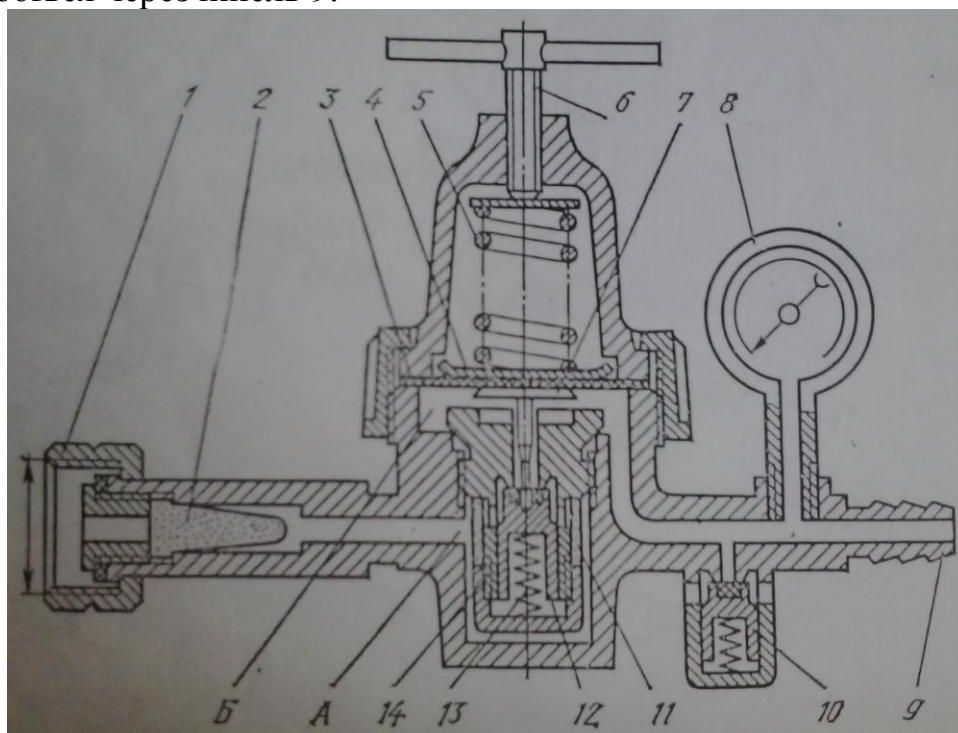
Схема пропан-бутанового редуктора ДПП – 1
